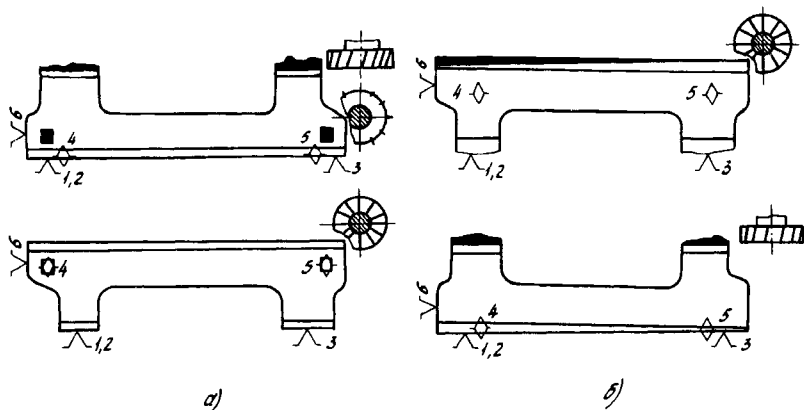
Обеспечение равномерного припуска на поверхностях направляющих станин
